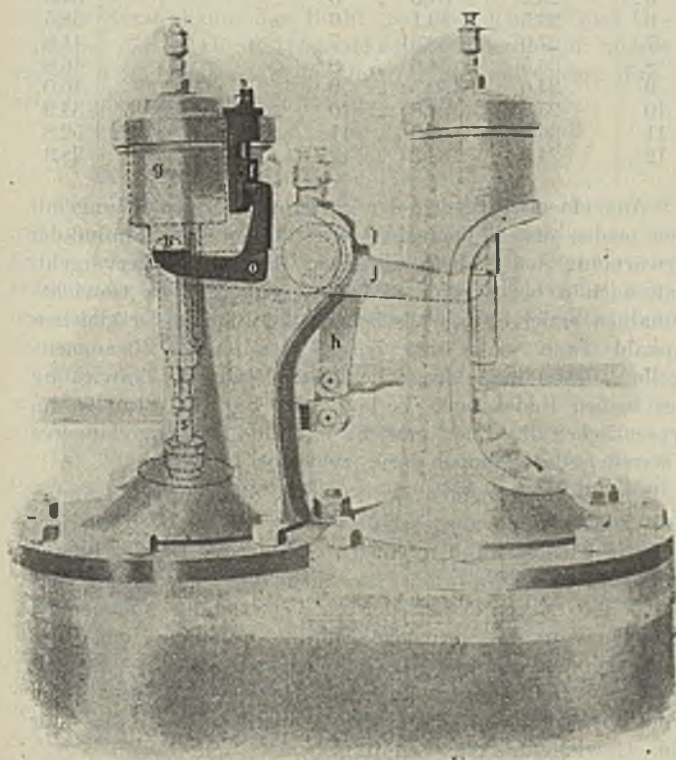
Kompressionsverminderer der Dingerschen Maschinenfabrik A.-G., Zweibrücken.
